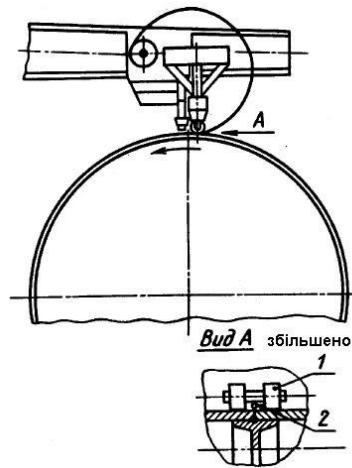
Прилад для притискання крайок до підкладного кільця перед зварювальною головкою
